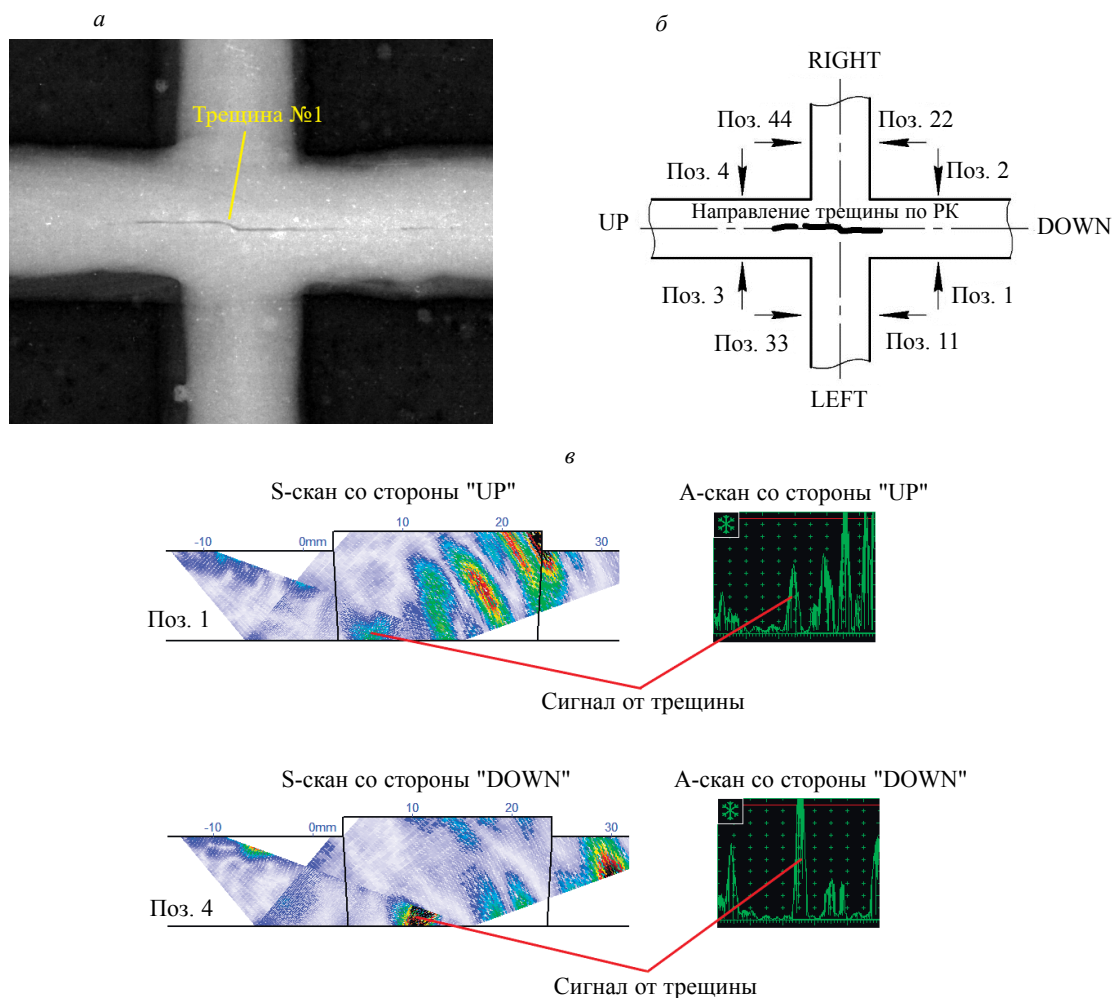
Выявление трещины № 1 в перекрестье сварных швов: рентгенограмма (а); схема сварного шва (б); выявление трещины наклонным ПЭП (в).
